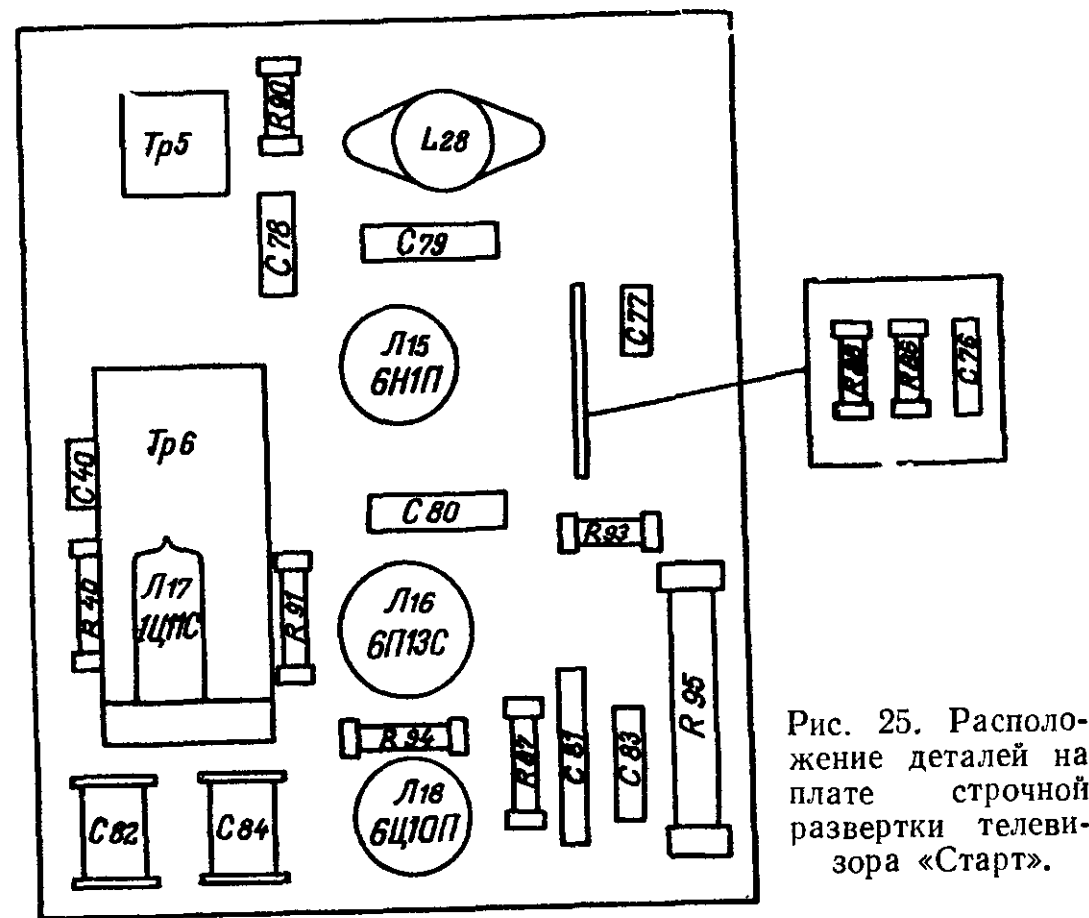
Расположение деталей на плате строчной развертки телевизора «Старт».
